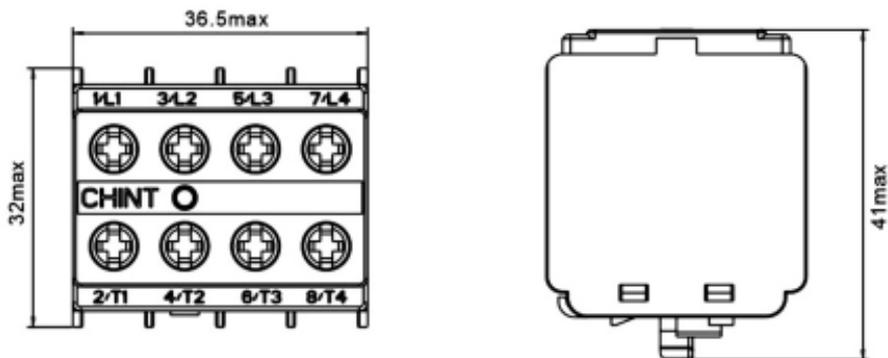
AX-3M辅助触头组安装尺寸与外形尺寸
